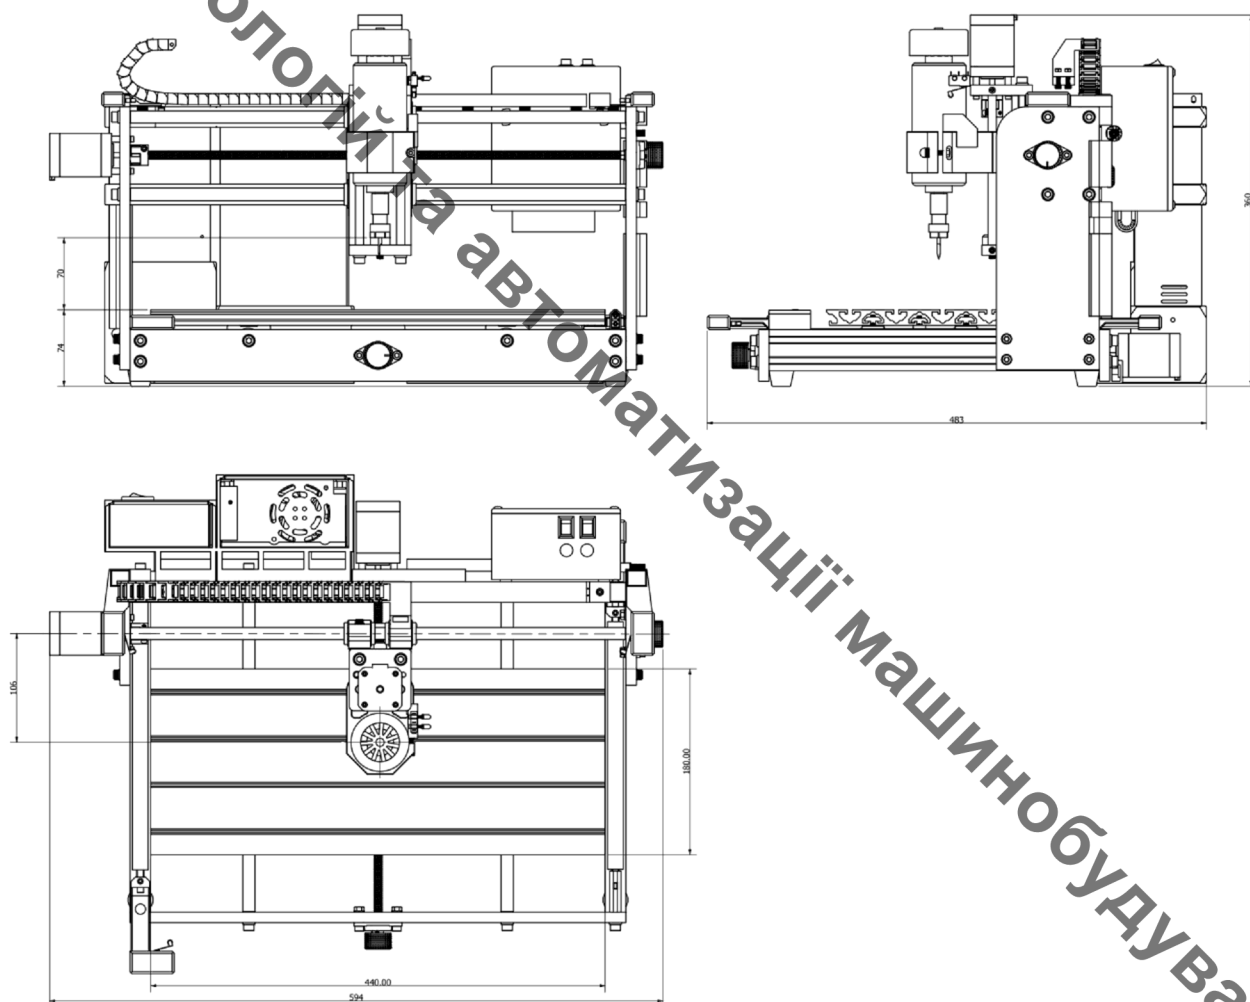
Складальне креслення прототипу фрезерно-гравірувального верстата з ЧПК моделі CNC 3018-Plus
